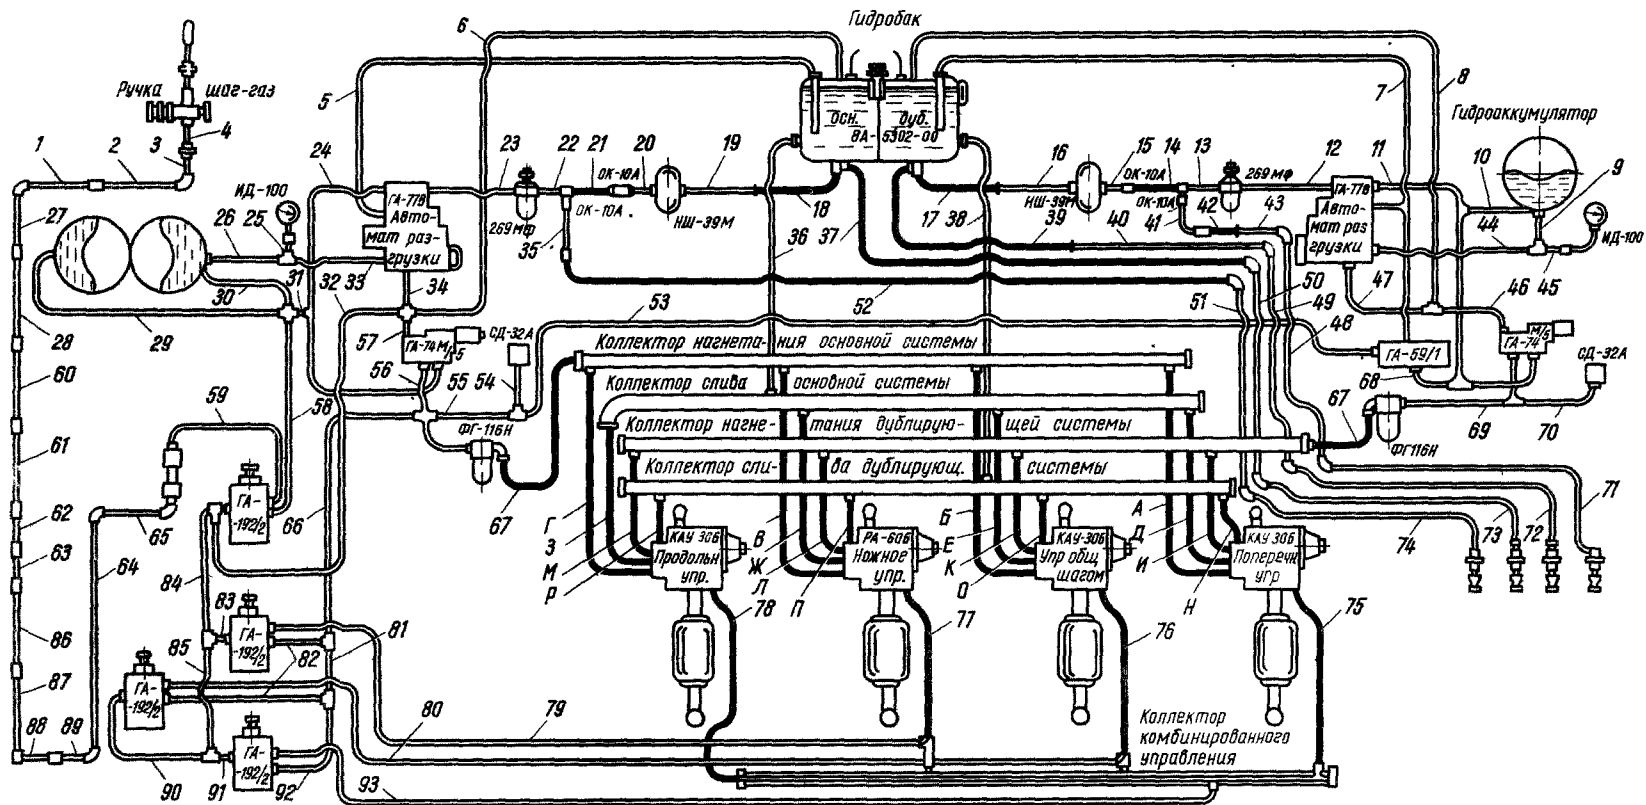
Схема гидросистемы (к таблицам трубопроводов и шлангов)
